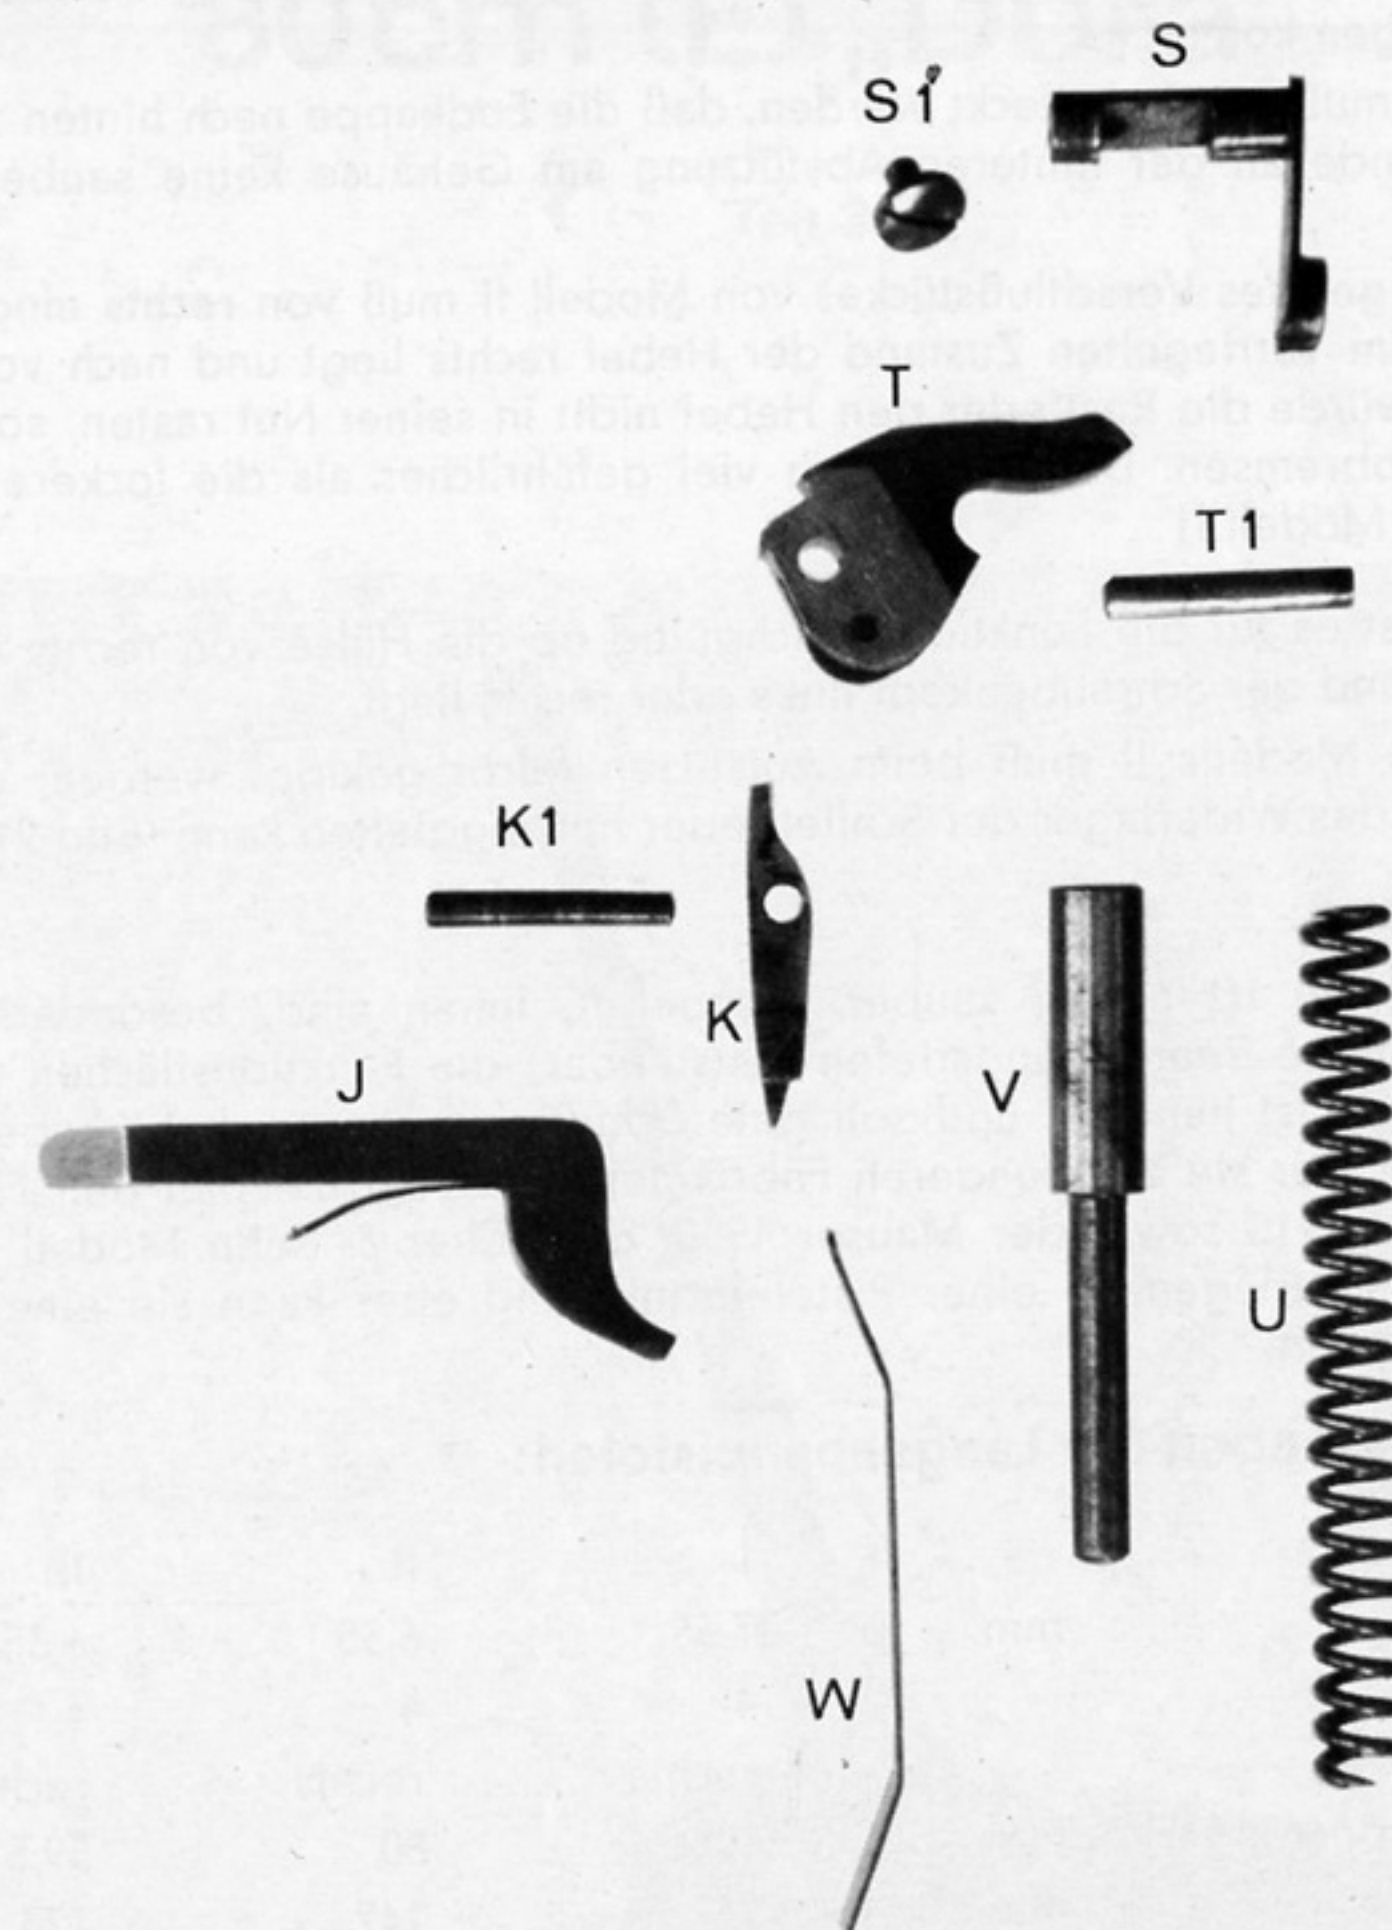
Teile des Schlosses und der Abzugseinrichtung von Modell I. J = Abzugdruckstange, K = Abzugstollen, K 1 = Abzugstollenachse, S = Sicherung, S 1 = Sicherungsschraube, T = Hammer, T 1 = Hammerachse, U = Schlagfeder, V = Druckkolben, W = Blattfeder für Abzugstollen und Magazinhalter.
